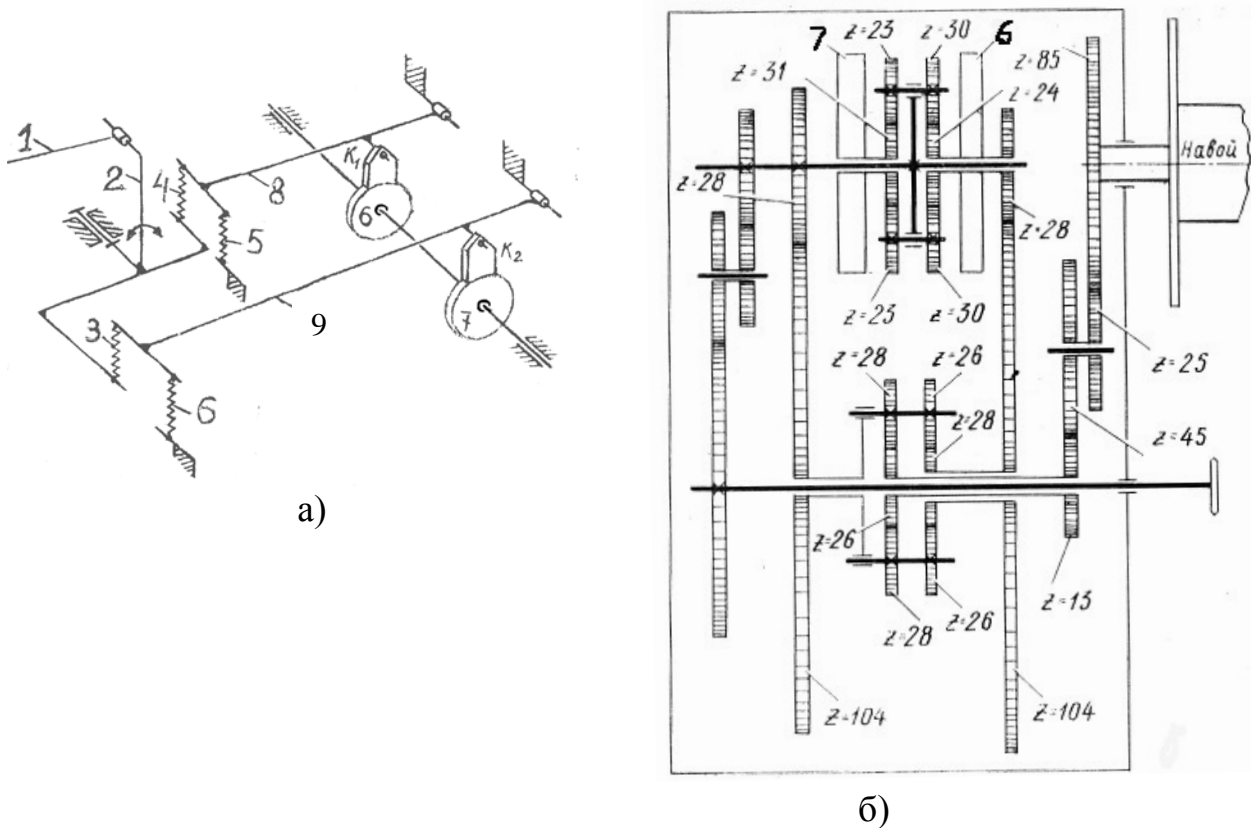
Устройство для изменения давления на тормозные диски редуктора (а) и разрез редукторной коробки (б) основовязальной машины «Кокетт-1»:
